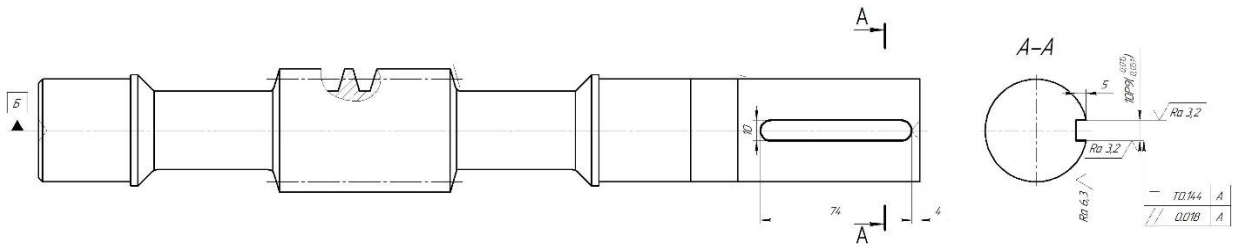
Ескіз обробки поверхонь на операцію 035 Фрезерна з ЧПК
